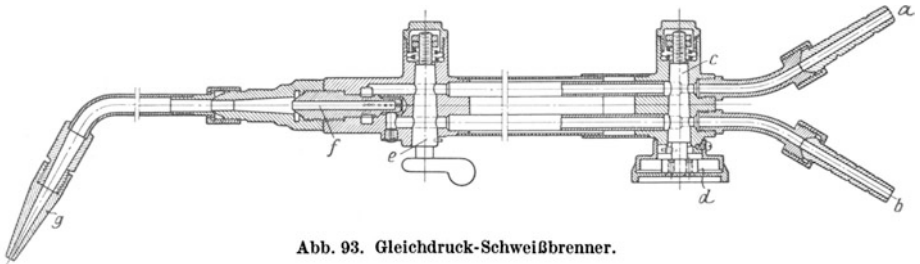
Gleichdruck-Schweißbrenner.
